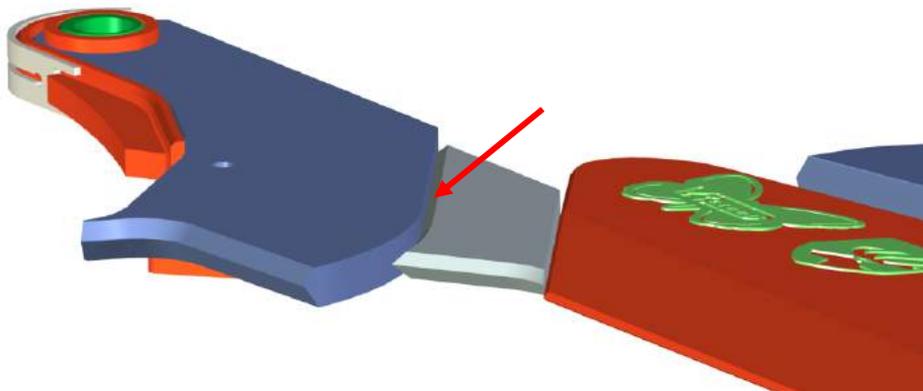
Ejemplo de buena práctica de alternar soldaduras en doble bisel (Lado A)
